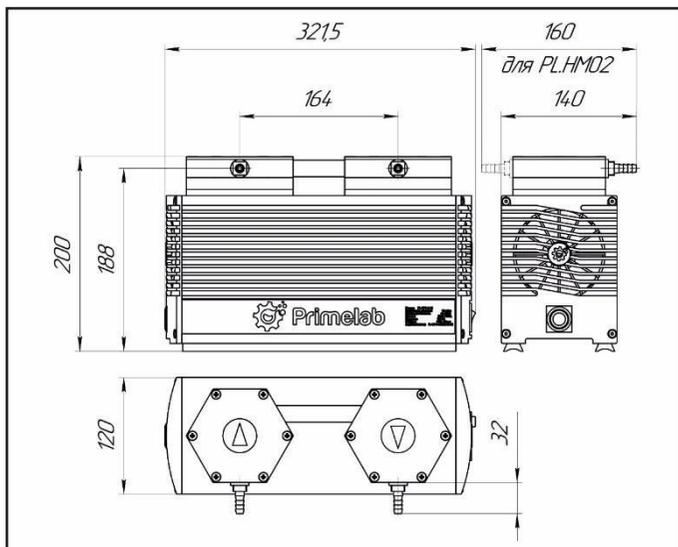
Габаритные размеры PL.HM01 и PL.HM02
